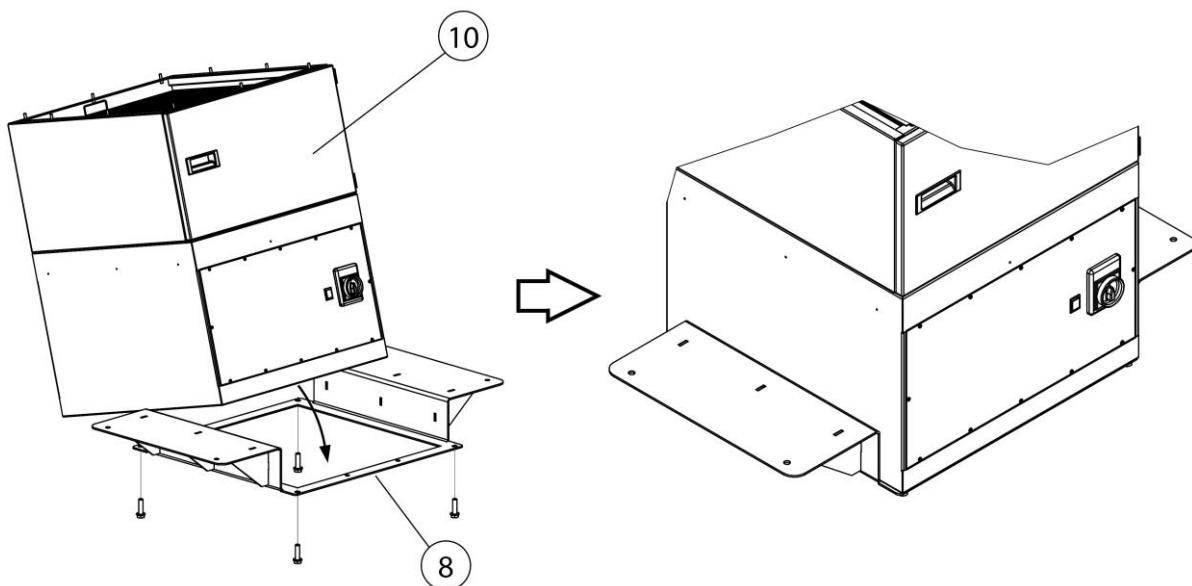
Montaggio – Montaggio del dispositivo di filtraggio sul telaio di supporto
